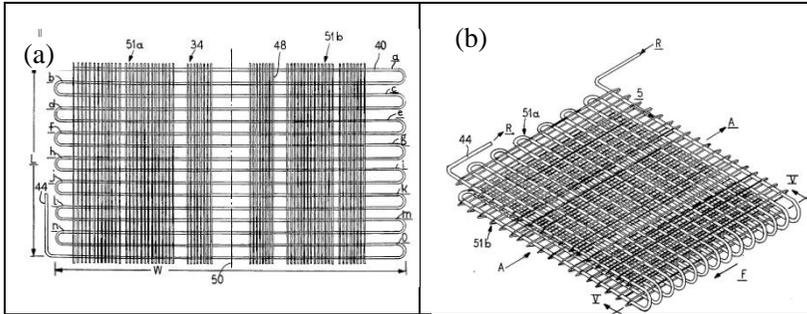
(a) Serpentina inicial com os arames soldados. (b) Trocador já dobrado e em sua configuração final (Dasher, 1996)
